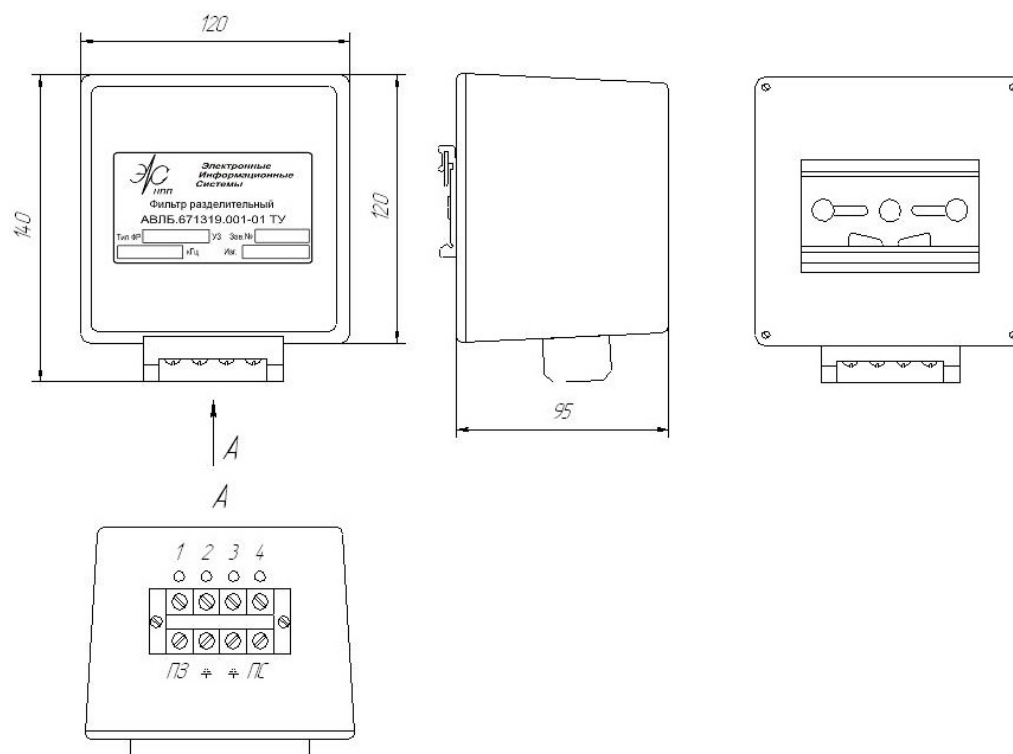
Габаритно-присоединительный чертеж фильтра присоединения ФП.
